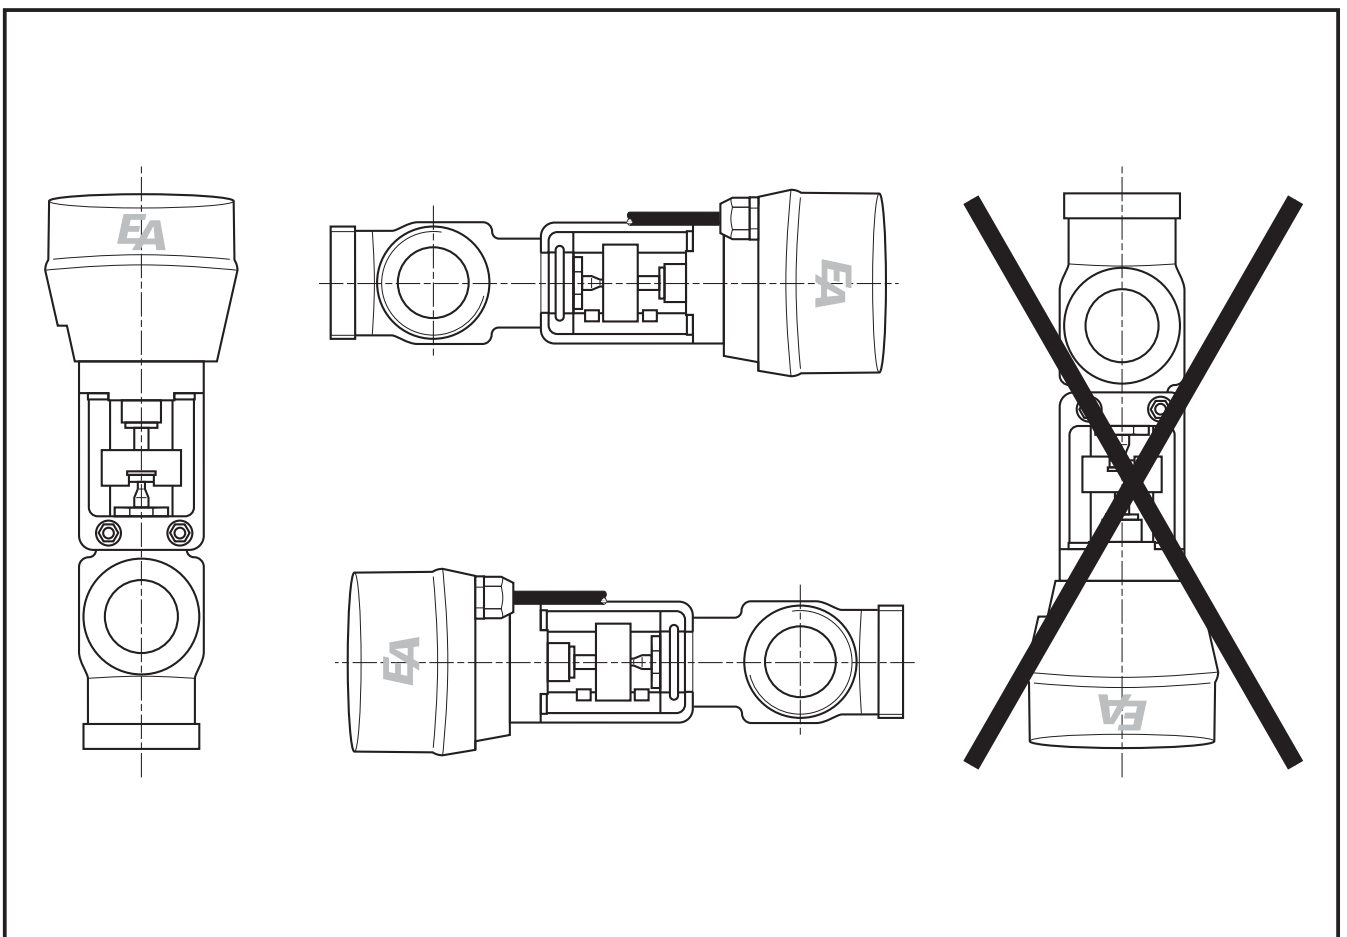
Beschreibung der Antriebe: Einbaulage Antrieb 21/23
